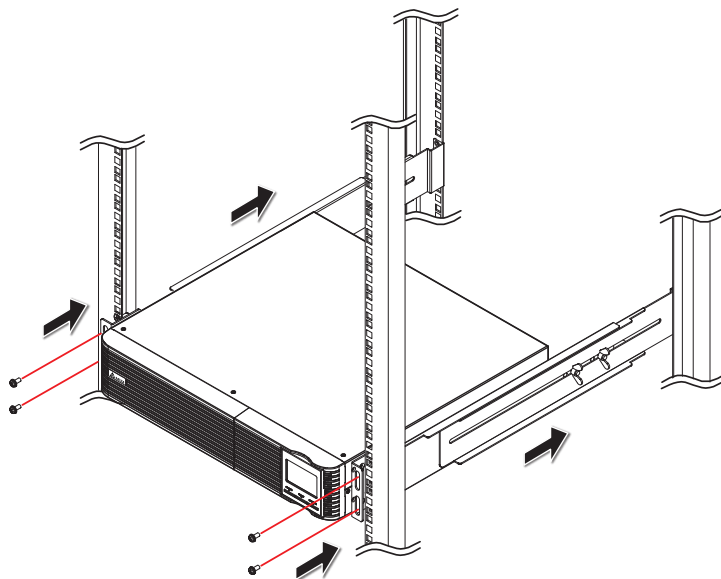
Регулировка длины направляющих и затяжка гаек)
